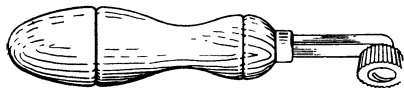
Рифленое колесико для декоративной накатки (размеры 8—10—12—14—16)
